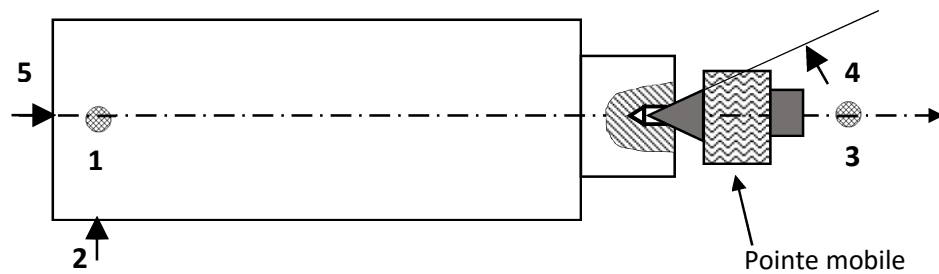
Mise en position d'un cylindre long en montage mixte sur un tour.
